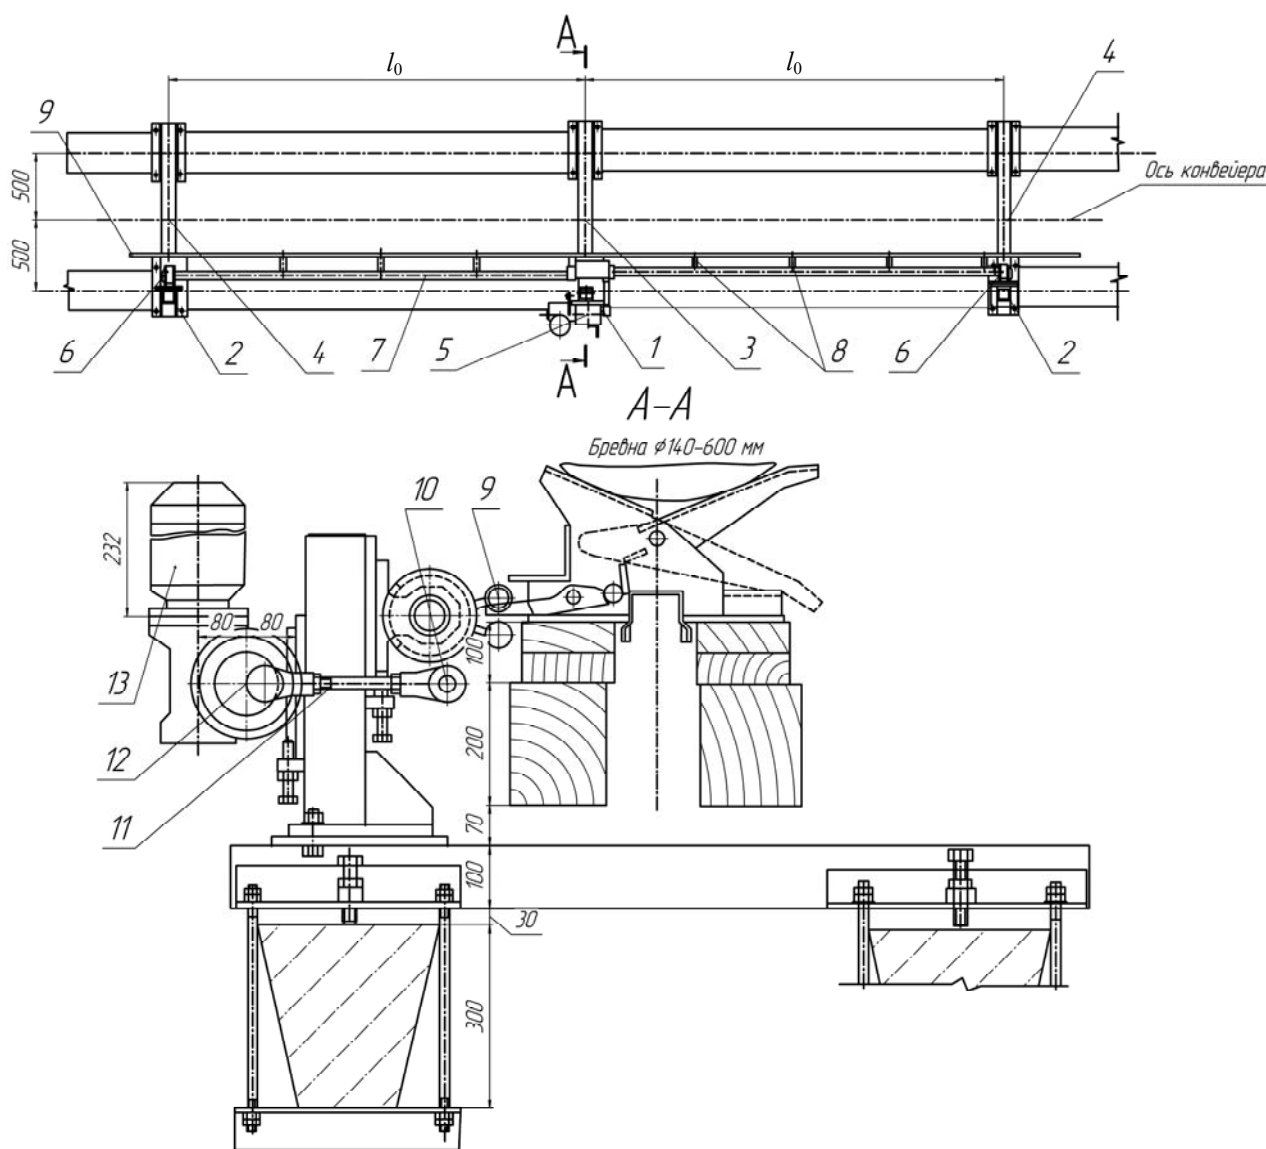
Шарнирно-рычажный механизм сбрасывателя
